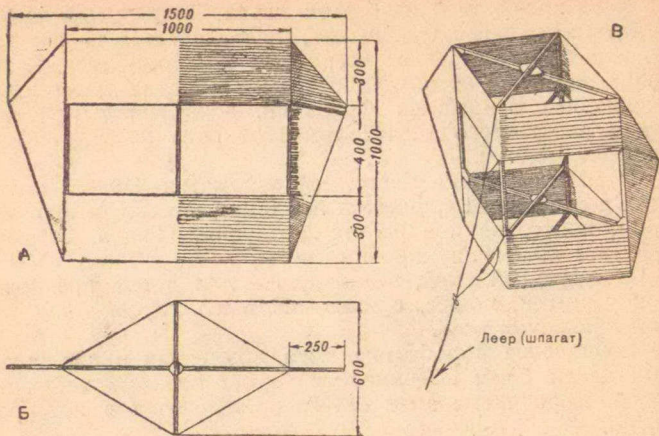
Воздушный коробчатый змей типа Поттера: А — вид сверху, Б — вид спереди, В — змей в полете.
